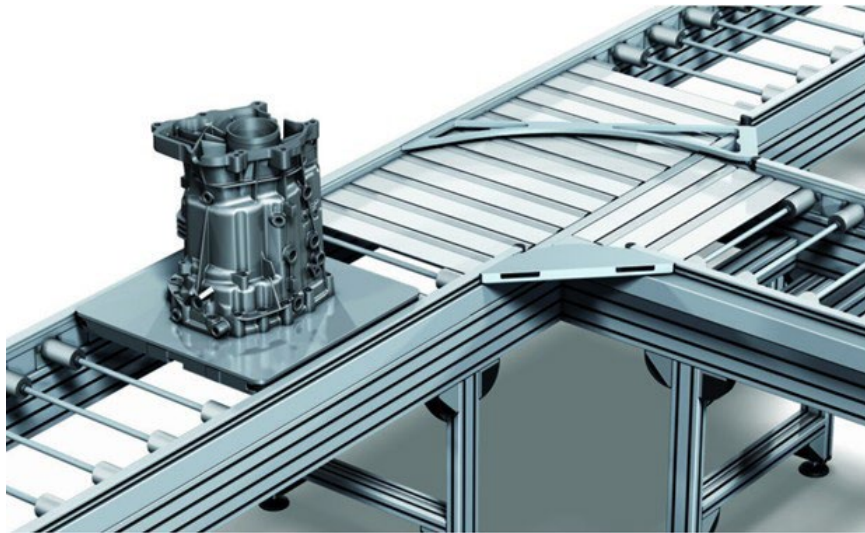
Sección de conveyor con pallet portando un motor (Factory of the Future Assembly, s. f.)
